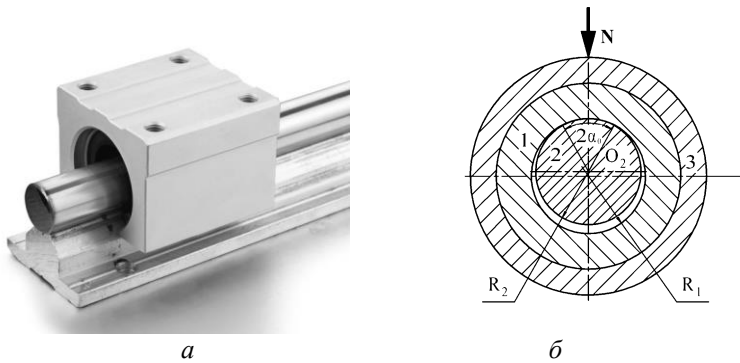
Циліндрична напрямна ковзання: а – загальний вигляд, б – розрахункова схема
